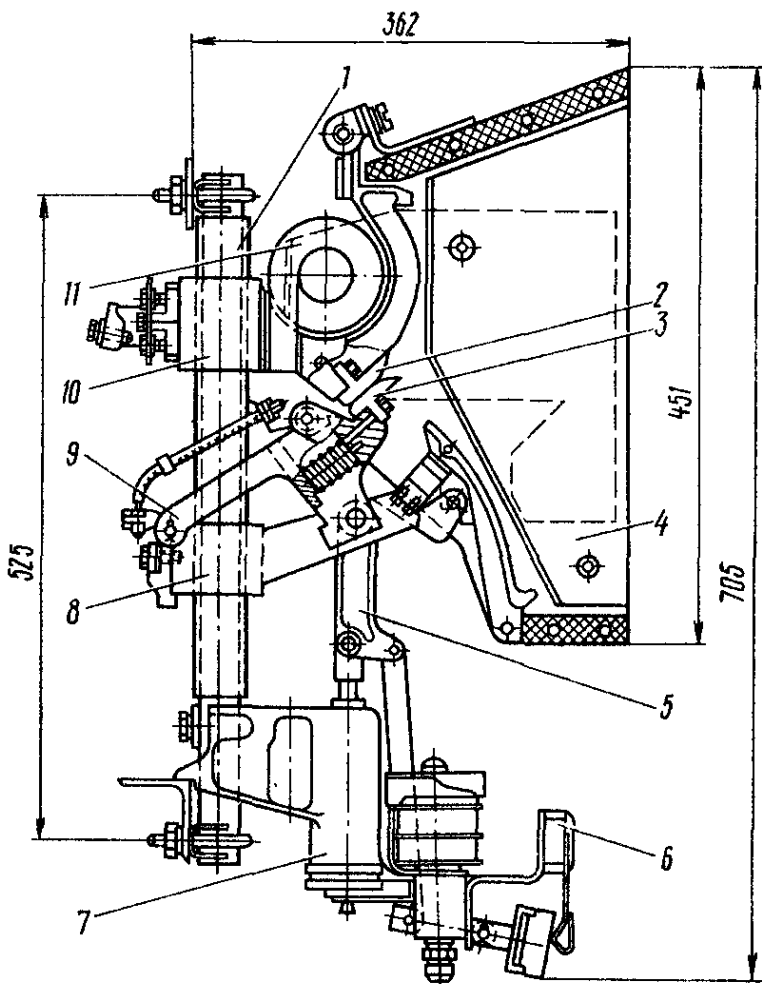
Электропневматический контактор ПК-06 (ПК-07-ПК-11):
